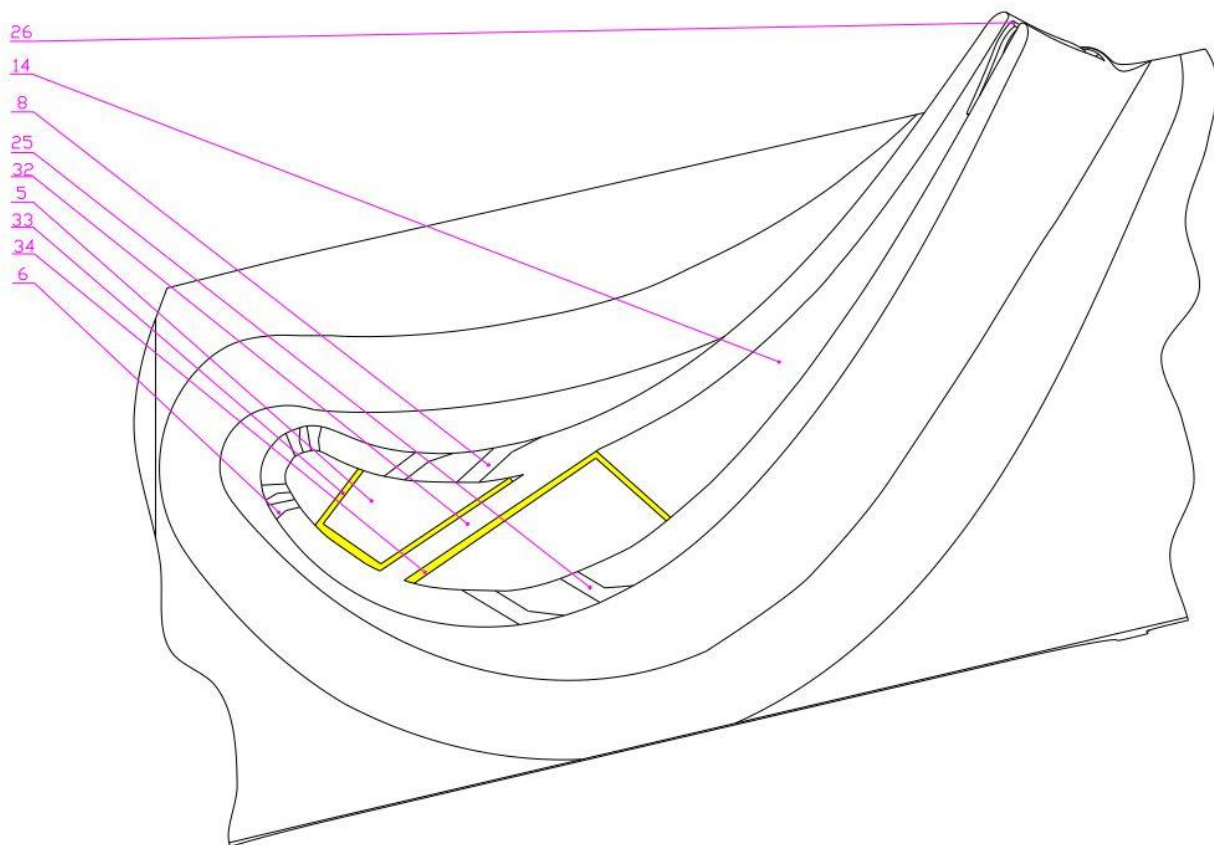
Продольный разрез профиля рабочей лопатки турбины
